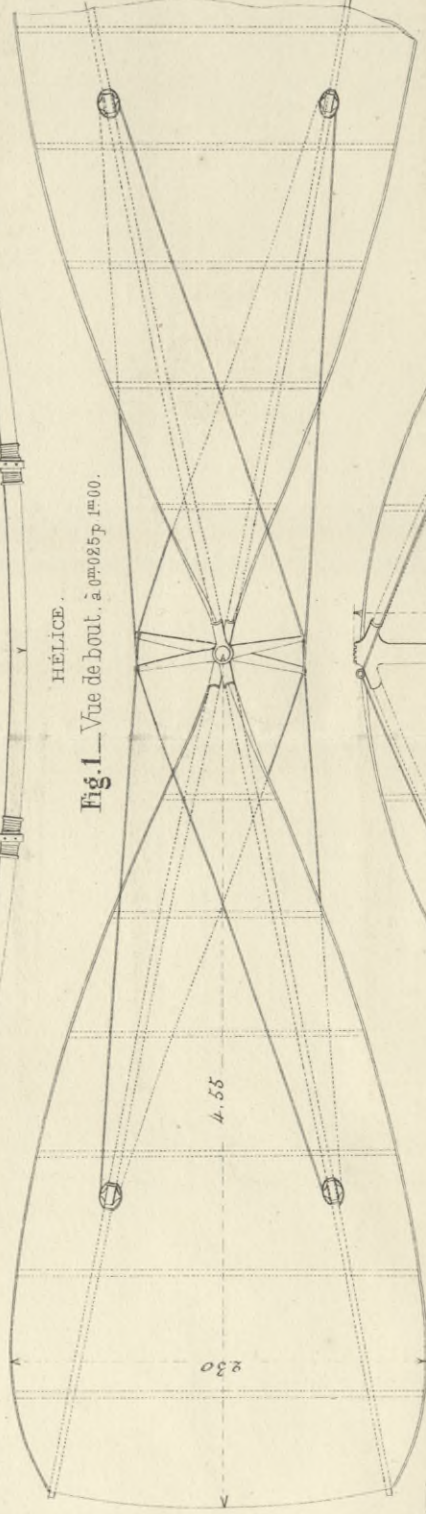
Vue de bout. à 0^m025 p. 1^m00.
